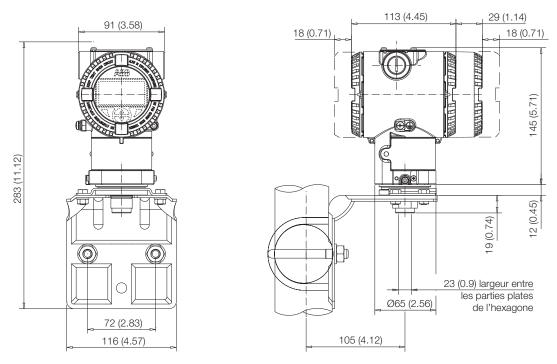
Modèle de transmetteur 266H ou 266N Hi de type P résistant à la surcharge équipé d'un capteur Z et d'un boîtier de type barillet installé sur un tuyau de 2" avec support de montage en option (B6 en acier au carbone ou B7 en acier inoxydable 316L)
